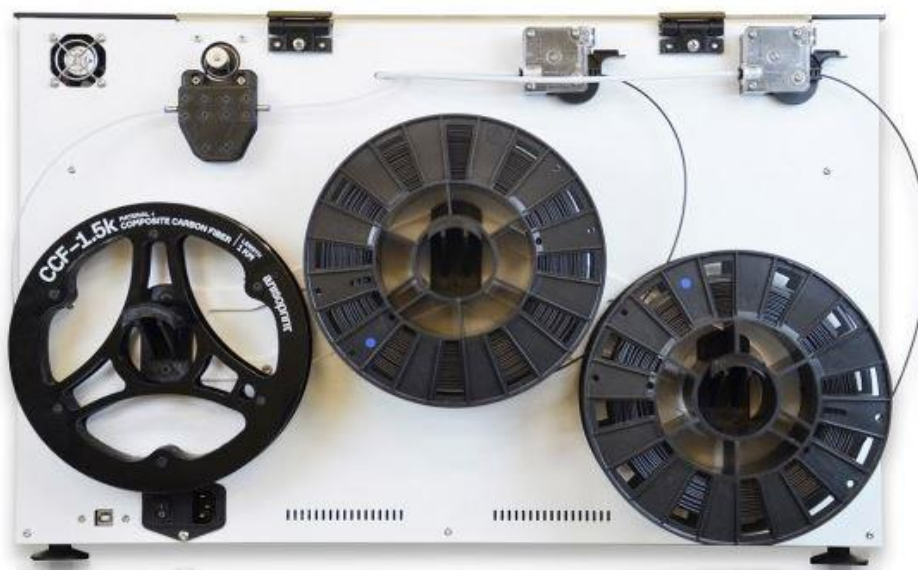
Retro dell'Anisoprint Composer A3 con le tre bobine di materiale
